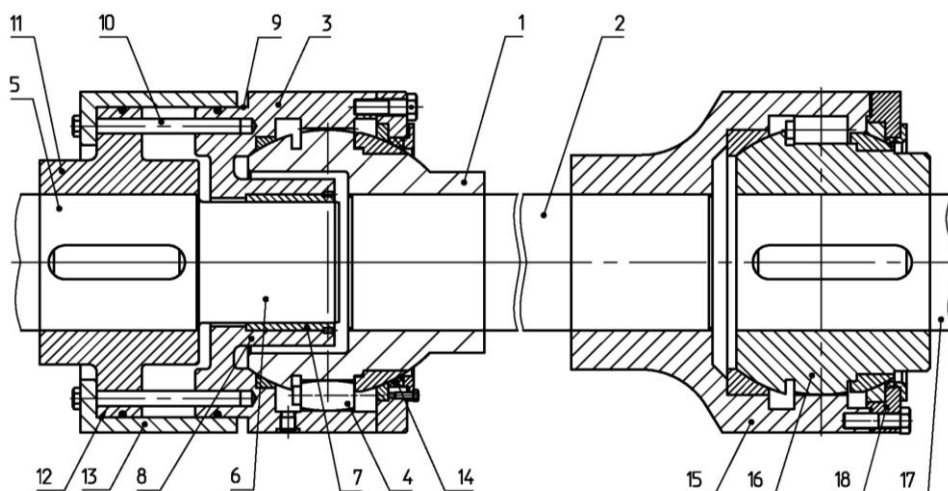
Базовая конструкция упругой муфты с роликовыми шарнирами
